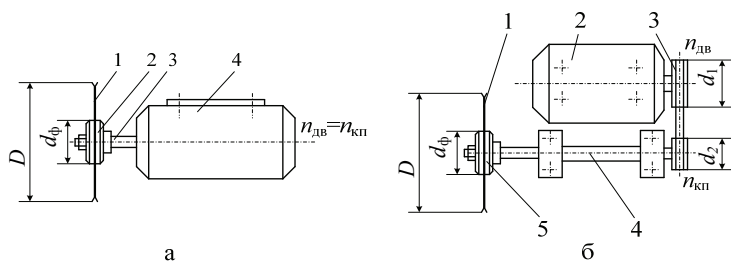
Схемы режущего механизма круглопильных станков: с удлиненным валом ротора (а) и с ременной передачей (б)
